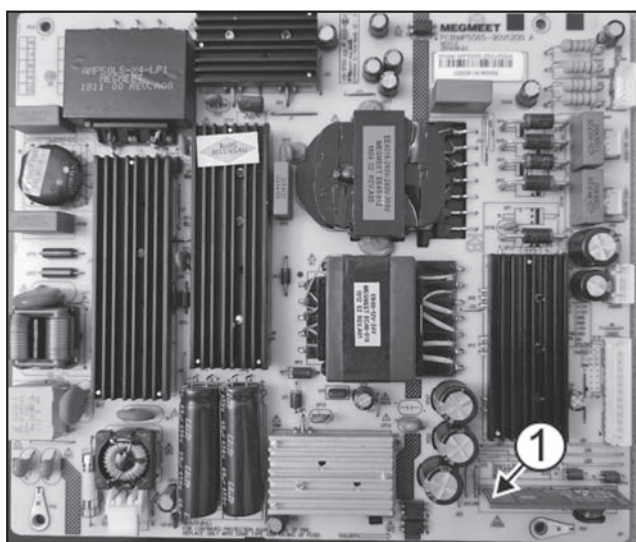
Внешний вид печатной платы MP5565-90V1200 (вид сверху), где 1 — модуль дежурного ИП (+5VSB)
